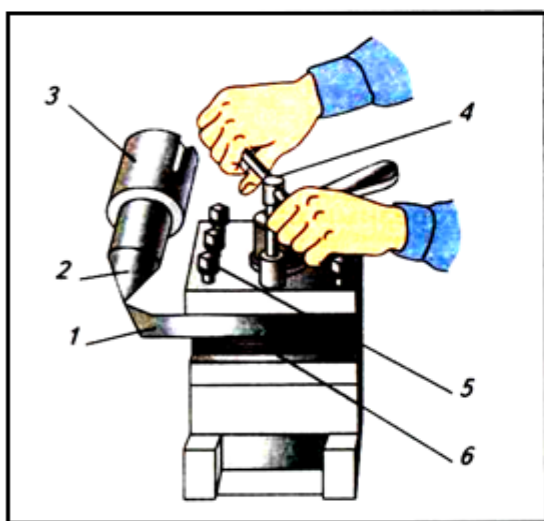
Установка токарного резца в резцедержателе: 1 – резец; 2 – задний центр; 3 – пиноль задней бабки; 4 – ключ; 5 – винты крепления резца; 6 – подкладка под резец
